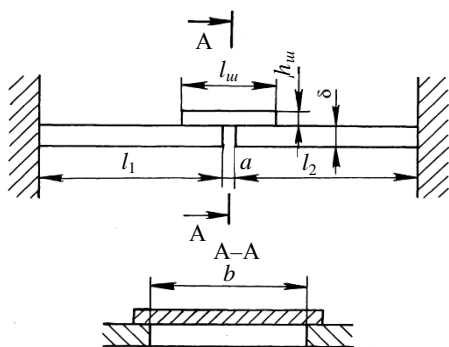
Схема сварного соединения при устранении трещины
